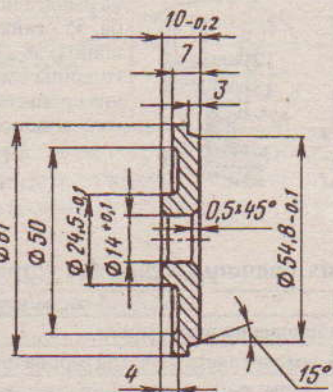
Оправка для запрессовки внутренних подшипников
